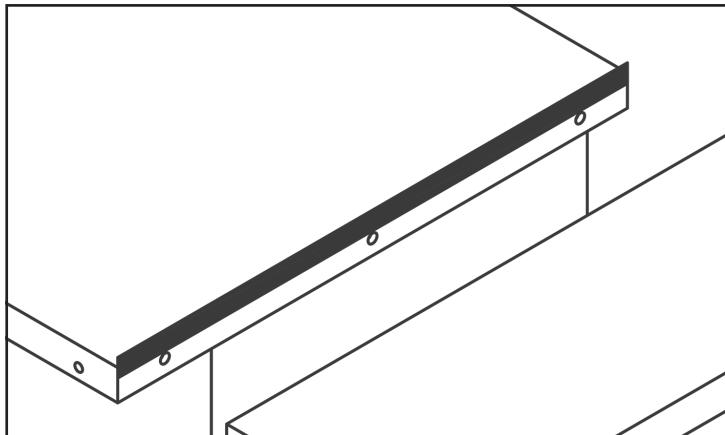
Colocación de cinta adhesiva para bajar el ala.
